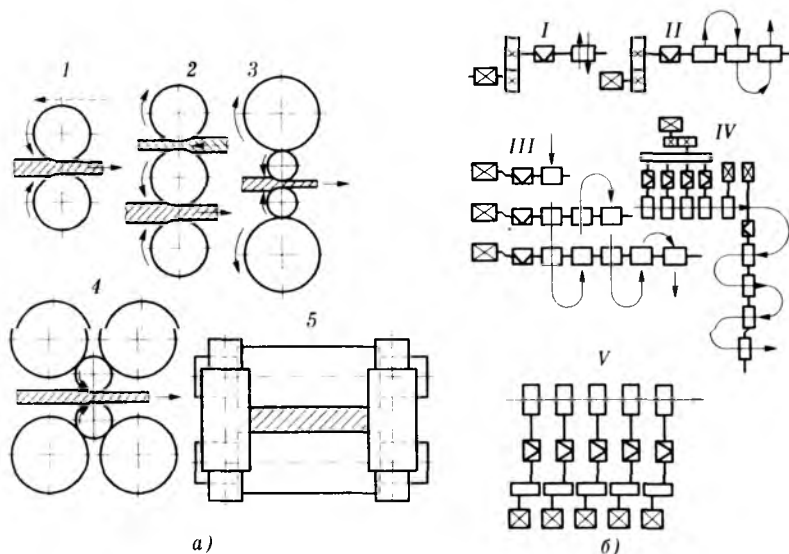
Схемы расположения валков и клеток в прокатных станах: а — схемы расположения валков; б — схемы расположения клеток;
